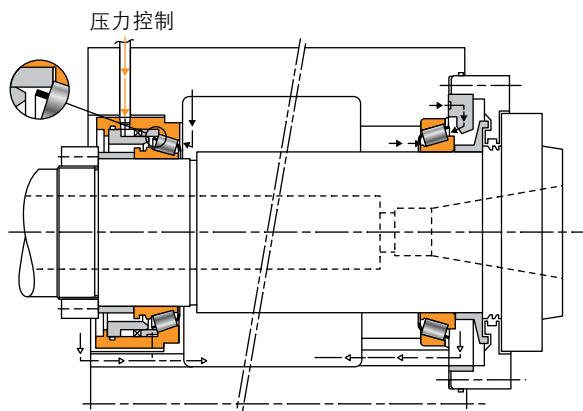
采用 Hydra-Rib 轴承 (有轴向进油冷却) 和 TS 轴承 (在滚子两端都有喷油孔用于进油和冷却) 的简易安装
